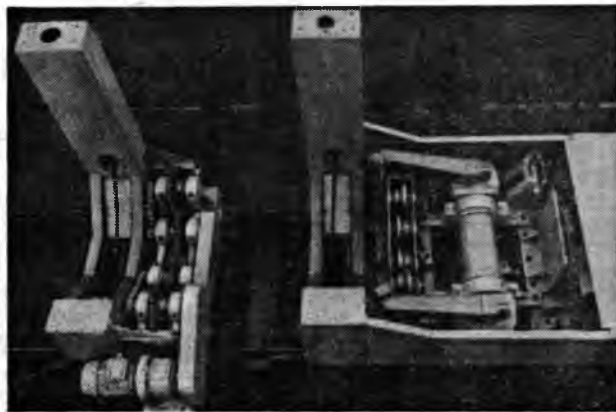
Манипулятор ПРТ80-2 (вид сверху)
